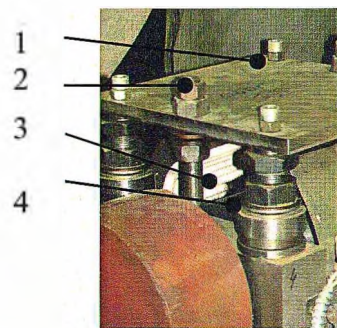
Узел уплотнения шпона: 1 – корпус, 2 – регулировочный клапан верхнего прессующего вала, 3 – инфракрасная лампа, 4 – верхний прессующий вал
